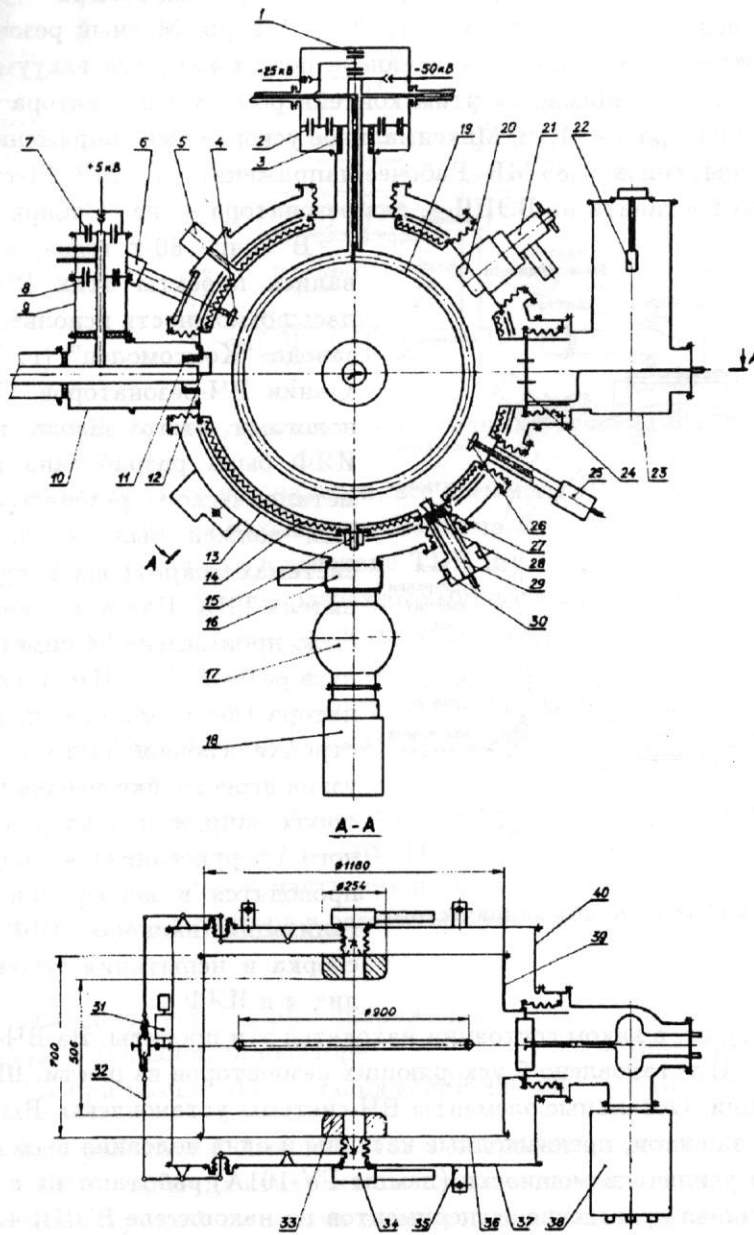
Схематический чертеж двухкамерного резонатора 181 МГц. 1, 2, 7, 8 – блокировочные конденсаторы; 3, 11, 28 – керамические изоляторы; 4, 20, 26 – элементы подстройки высших мод; 6, 21, 25 – приводы подстройки; 5 – вывод нагревателей и термпар; 9 – четвертьволновый стакан; 10 – узел ввода мощности; 12 – петля связи; 13 – тепловые экраны; 14 – нагреватели; 15 – перепускной клапан; 16, 34 – вакуумные шиберы; 17 – азотная ловушка; 18, 38 – магниторазрядные насосы; 19 – противоразрядное кольцо; 22 – испаритель титана; 23 – сорбционный насос; 24 – электромагнитный экран; 27 – измерительная петля; 29 – отрезок коаксиальной линии; 30 – датчики напряжения; 31 – привод подстройки основной частоты; 32 – механизм подстройки; 33, 36, 39 – корпус резонатора; 37, 40 – вакуумный кожух; 35 – геодезические знаки.
